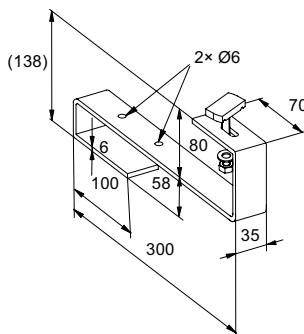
Odkrytie priestoru pre inštaláciu háku
